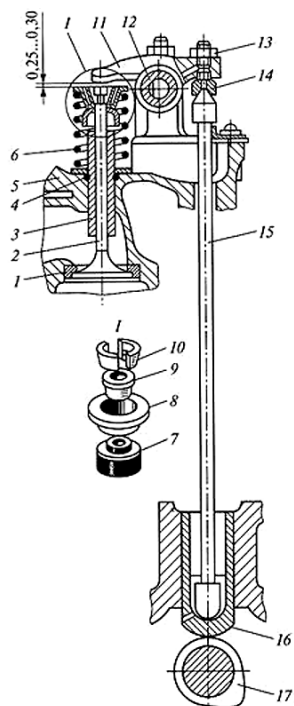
Схема газораспределительного механизма с верхним расположением клапанов: 1 – седло; 2 – клапан; 3 – направляющая втулка; 4 – стопорное кольцо; 5 – головка цилиндров; 6 – пружина; 7 – уплотнительный колпачок; 8 – тарелка; 9 – втулка; 10 – сухарики; 11 – коромысло; 12 – ось; 13 – контргайка; 14 – регулировочный винт; 15 – штанга; 16 – толкатель; 17 – кулачок
